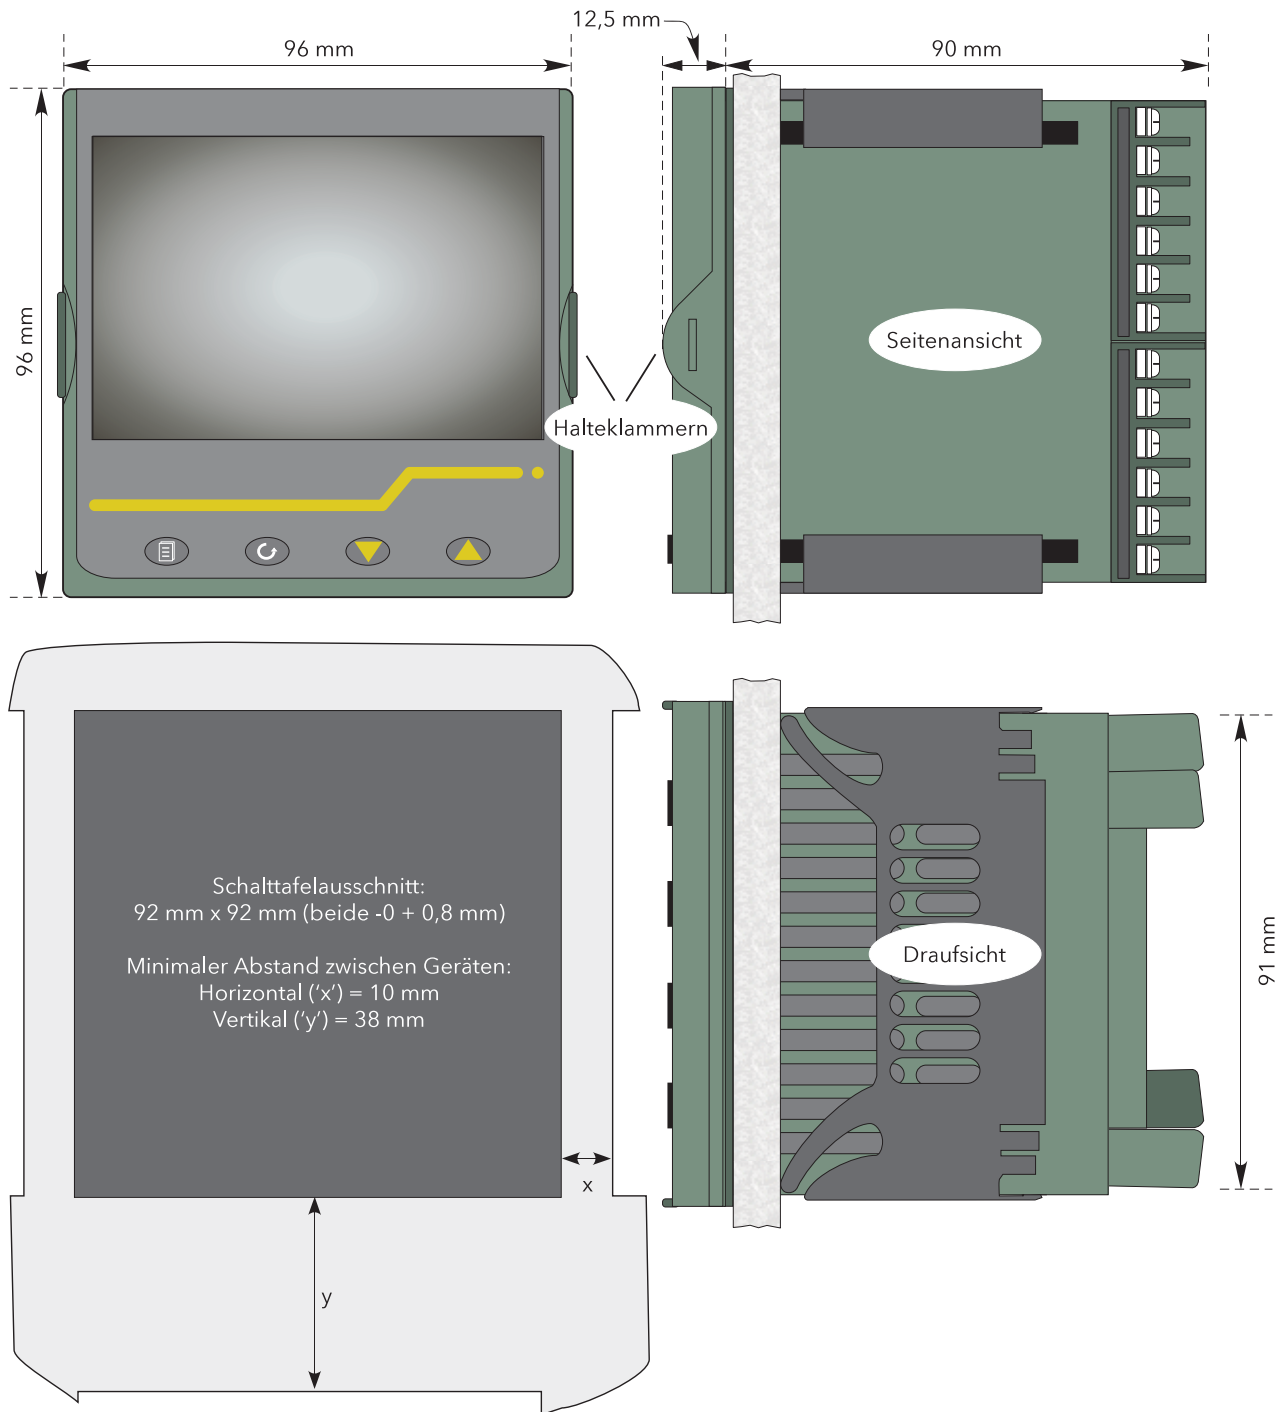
Details zur mechanischen Installation (Gehäuse mit abwaschbarer Front)
